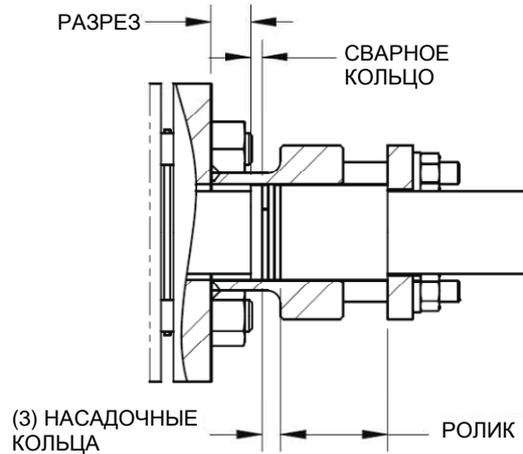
иллюстрирует вид Annubar Flange-Lok по завершении установки. Пожалуйста, обратите внимание, что между корпусом Flange-Lok и сварным кольцом должен быть зазор.
